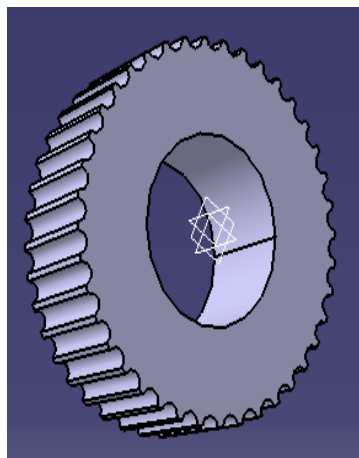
PIÑÓN SISTEMA DE ELEVACIÓN
